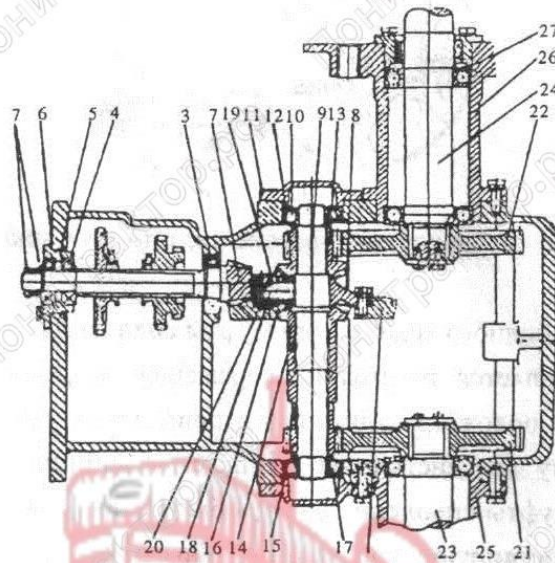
Схема конструкции заднего моста: 1-ведомая коническая шестерня; 2-ведущая коническая шестерня; 3-подшипник 90906; 4-подшипник 7205; 5-стакан подшипника; 6- прокладки; 7-регулирующая и стопорная гайка; 8-крестовина сателлита дифференциала; 9-ось центральной передачи; 10-подшипник 7306; 11-крышка подшипника; 12- регулировочные прокладки; 13-шестерня правой полуоси; 14-шестерня левой полуоси; 15- ведущая шестерня конечной передачи; 16-планетарная шестерня; 17-антифрикционная прокладка; 18-ось планетарной шестерни; 19-антифрикционная прокладка; 20-штифт; 21,22- ведомые шестерни левой и правой конечных передач; 23, 24-левая и правая оси ведущих колес 25,26-корпусы левой и правой полуоси 27-регулирующие прокладки.
